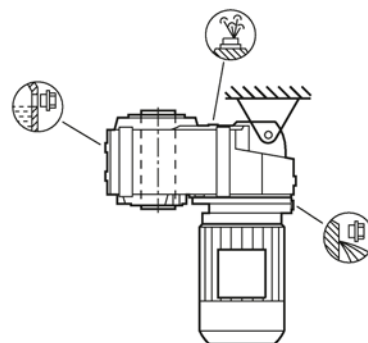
Монтажные положения для плоского редуктора F.AD в насадном исполнении, типоразмер 29
